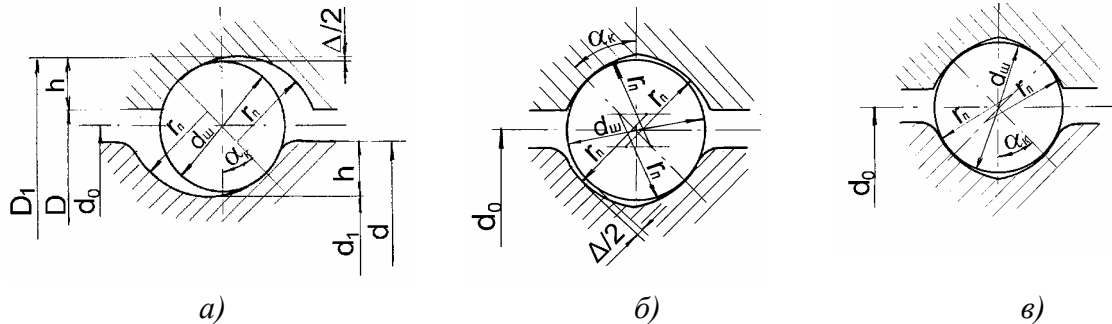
Профили резьбы винта и гайки шариковых винтовых передач
